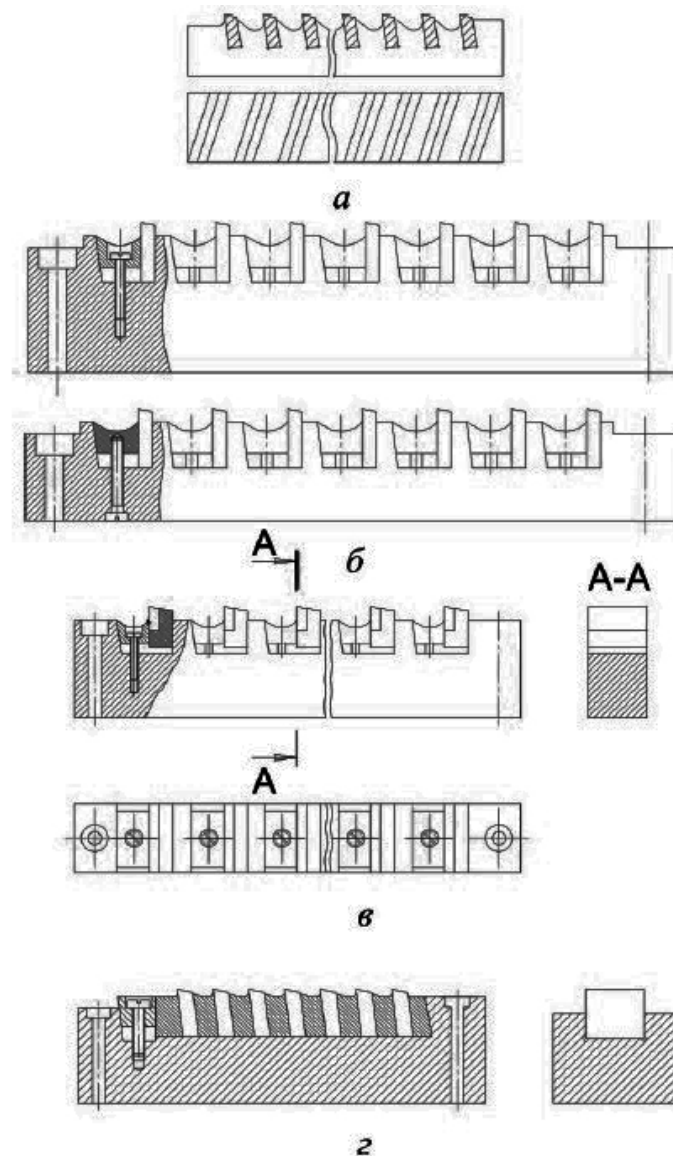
Нероз'ємне з'єднання зубців протяжки з корпусом (*a*);
